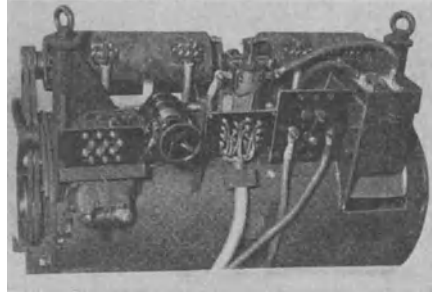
Schweißdynamo mit Steuermotoren für Automaten.
